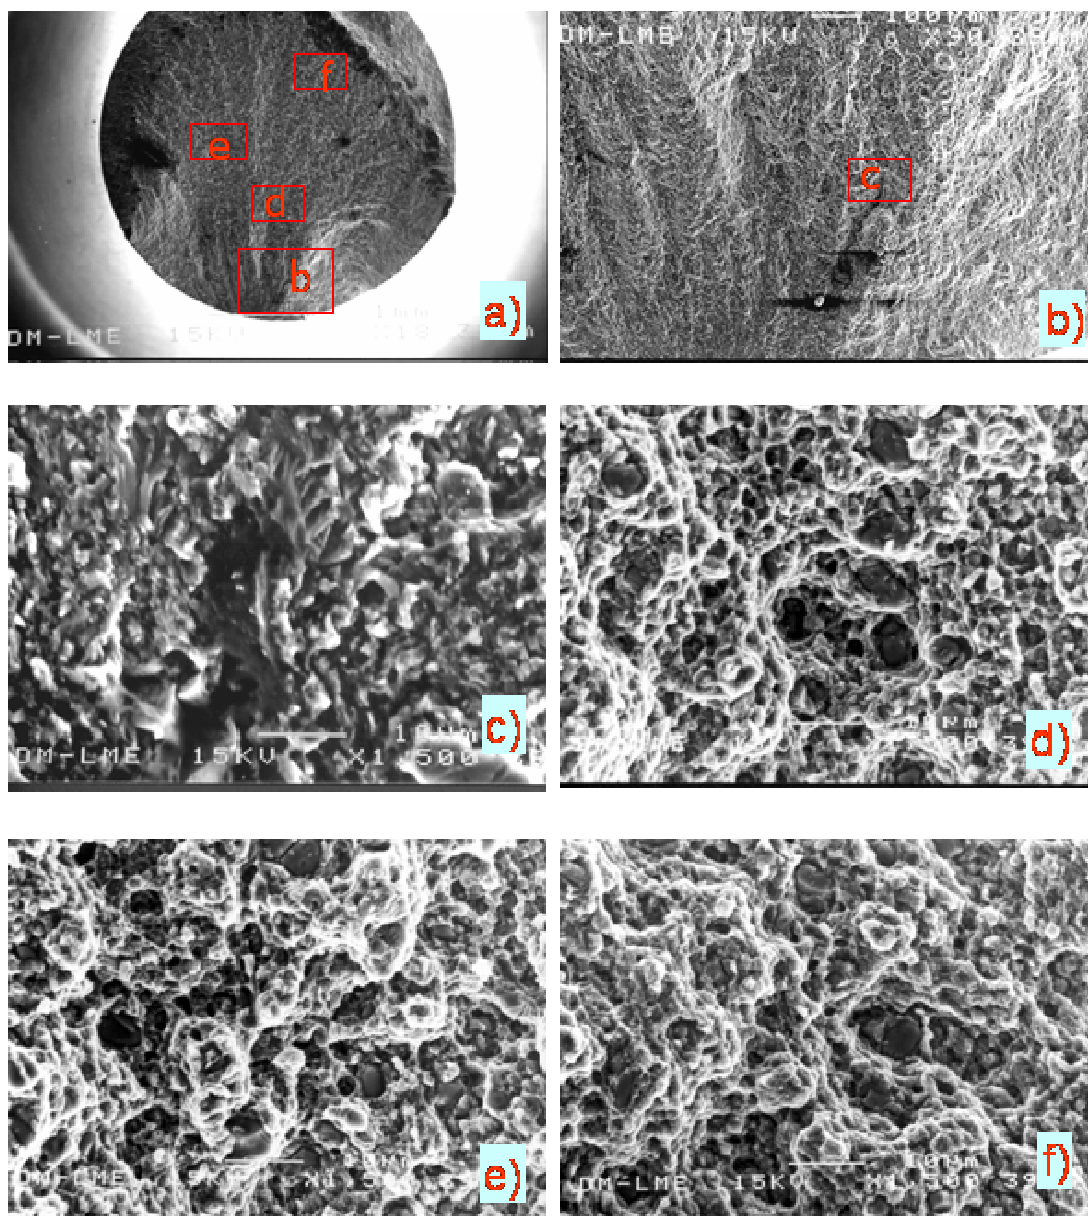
Superficie de probeta entallada de fatiga del material compuesto A2124/SiC/17p T4, fracturada a 400400 ciclos, solicitada a una tensión máxima de 375 MPa y para una R de 0,6: a) aspecto general; b) zona de inicio, mostrando grietas secundarias; c) ampliación de la región b, mostrando deformación severa en la matriz, d) zona de la región de Paris, mostrando microductilidad generalizada, e) zona media de la región de Paris y, f) zonal final de la región de Paris.
